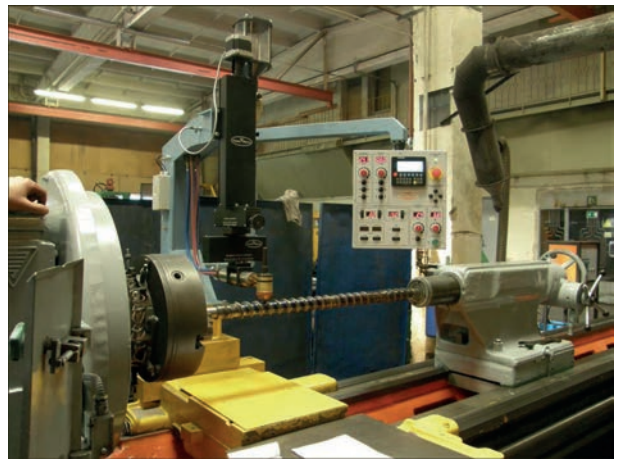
Установка для плазменно-порошковой наплавки на базе токарно-винторезного станка и аппарата РМ-300
